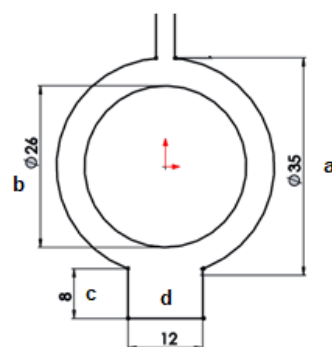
Vista lateral del barril y la chaqueta metálica.
